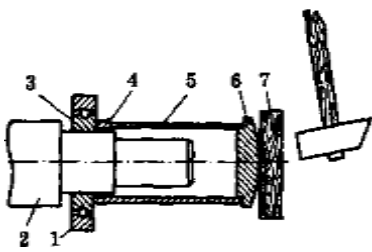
Процесс насадки на вал: 1 — наружная обойма подшипника; 2 — вал; 3 — внутренняя обойма подшипника; 4 — медный ободок; 5 — моктажная трубка; 6 — металлическая пробка; 7 — молоток.
